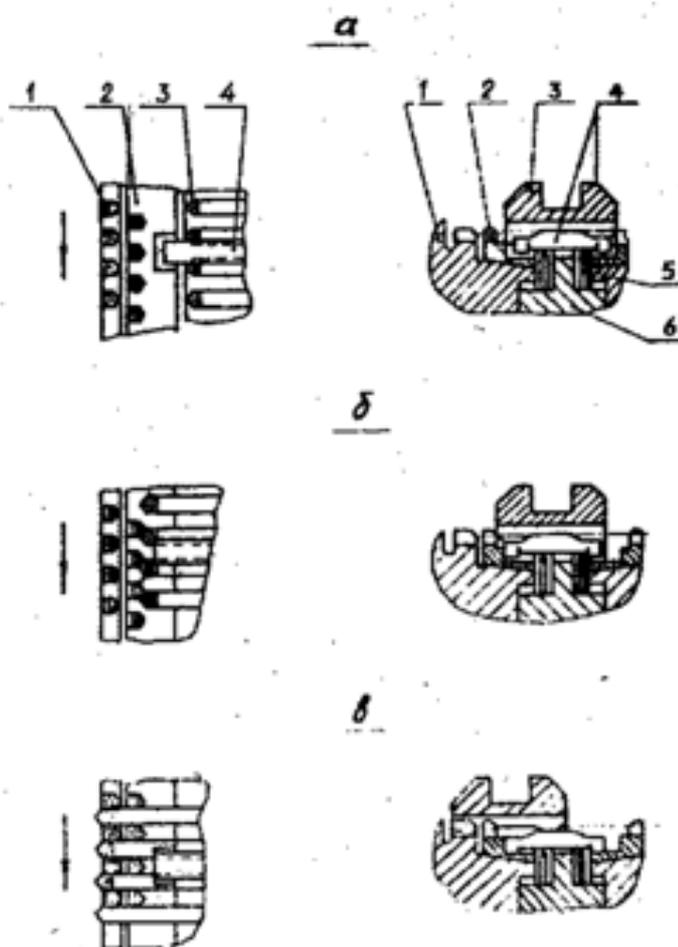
Схема работы синхронизатора: 1 - зубчатый венец шестерни; 2 - блокирующее кольцо синхронизатора; 3 - муфта синхронизатора; 4 - сухарь синхронизатора; 5 - пружина синхронизатора; 6 - ступица синхронизатора; а - нейтральное положение передач; б - начало синхронизации; в - передача включена
